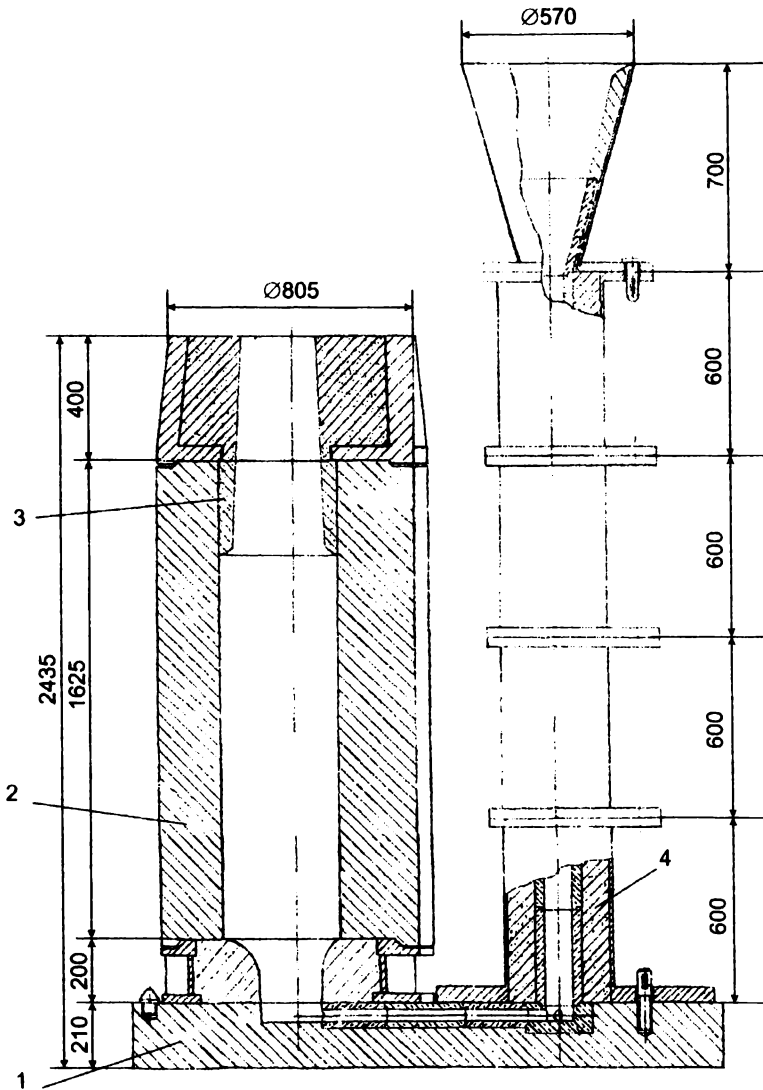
Форма в сборе для литья гладкой заготовки (вид сбоку):
